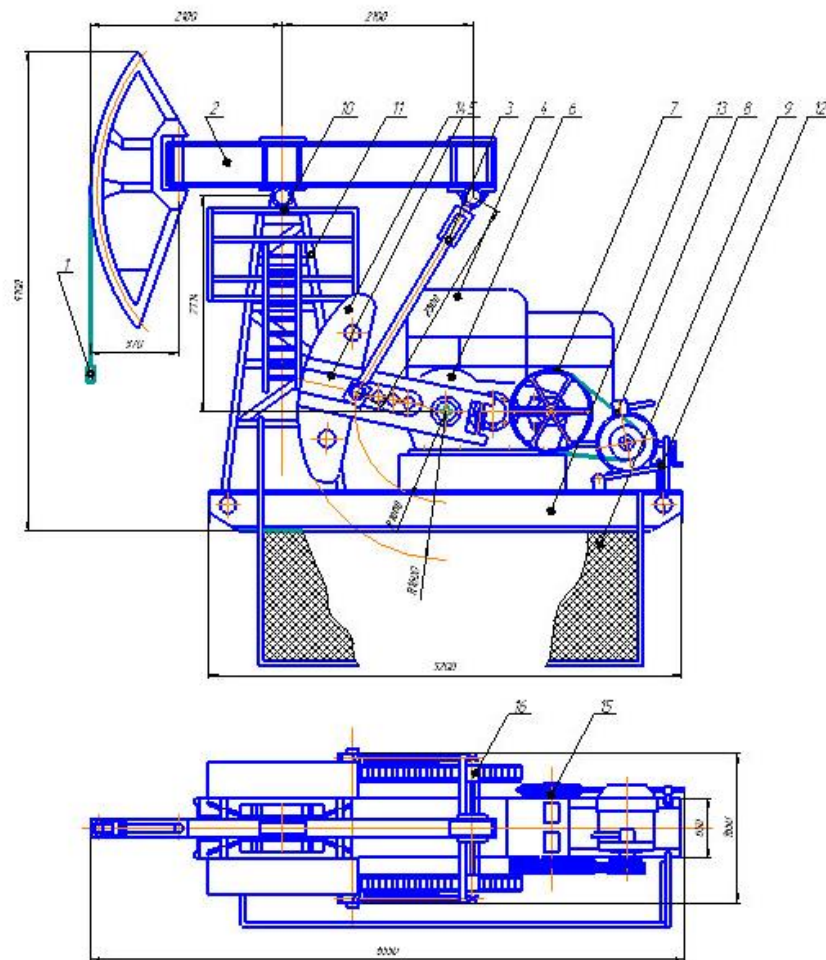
Станок-качалка СКД 6-2,1-2500
